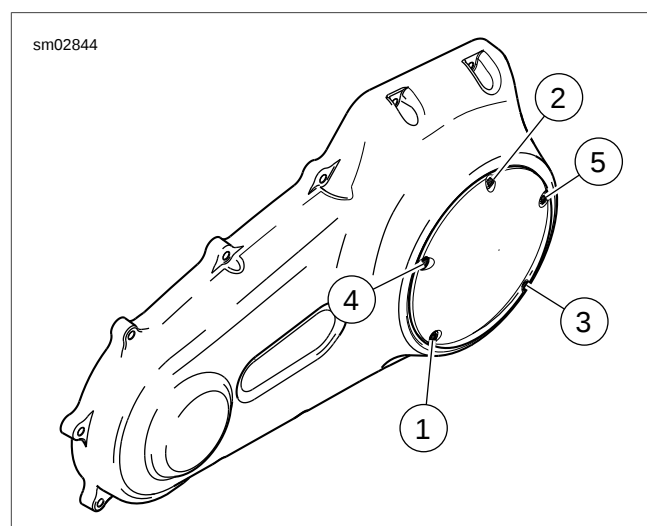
Séquence de serrage de couvercle d'embrayage
